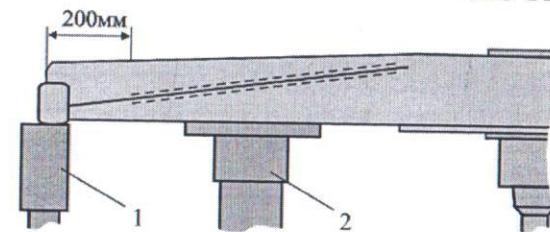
Контроль околошовной зоны сварного соединения накладок с верхними поясами продольных балок рамы
